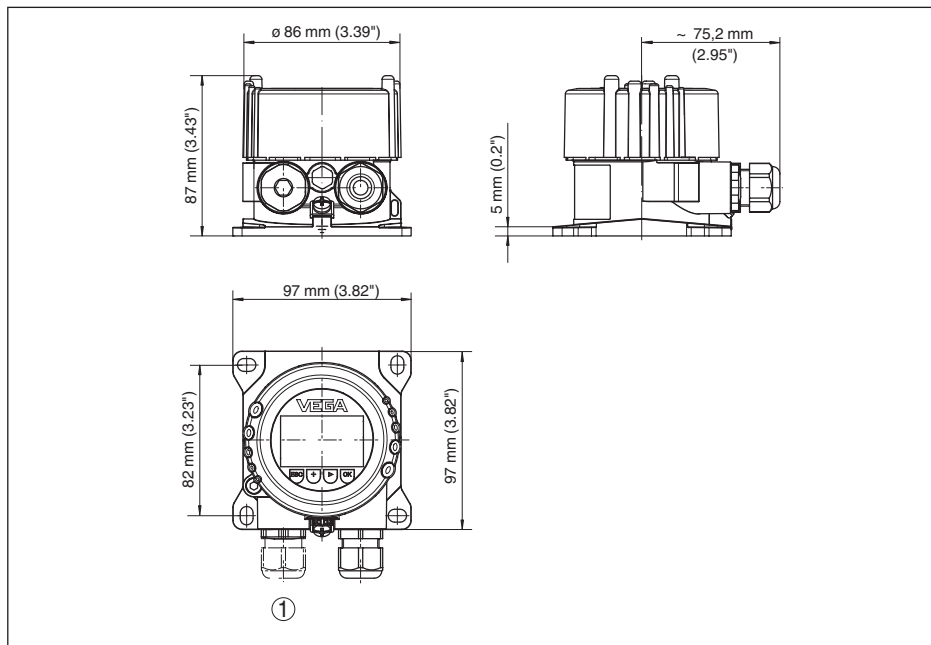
VEGADIS 81 с алюминиевым корпусом
